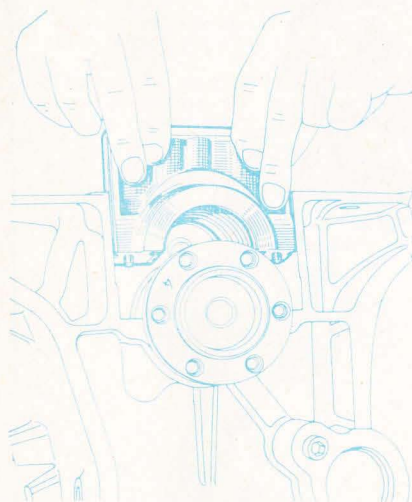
Montage du chapeau de palier arrière équipé de son demi-coussinet
